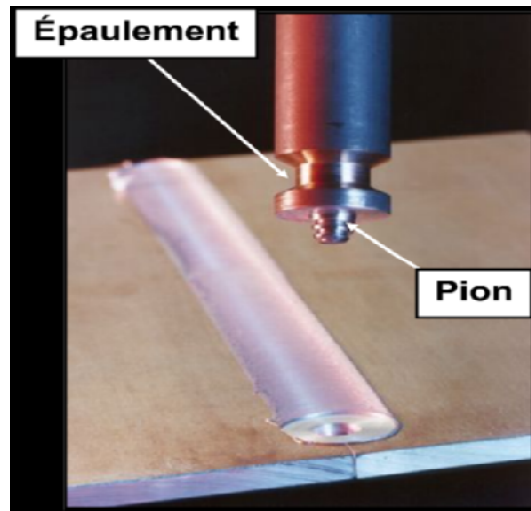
Principales composantes de l'outil de soudage
